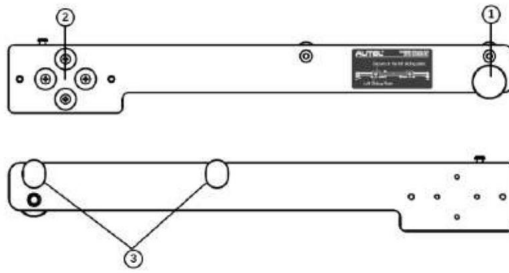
Varilla de extensión izquierda AUTEL-CSC050A/18_L
